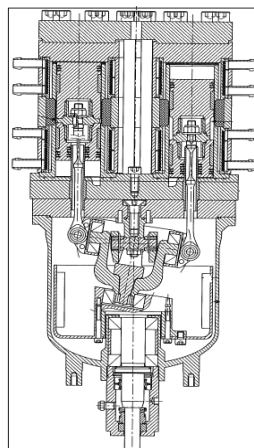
version modifiée, par David Haywood, du moteur double effet en machine réceptrice [29].
